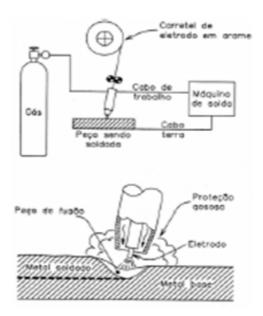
Ilustração de um processo de soldagem por MIG/MAG – GMAW.
